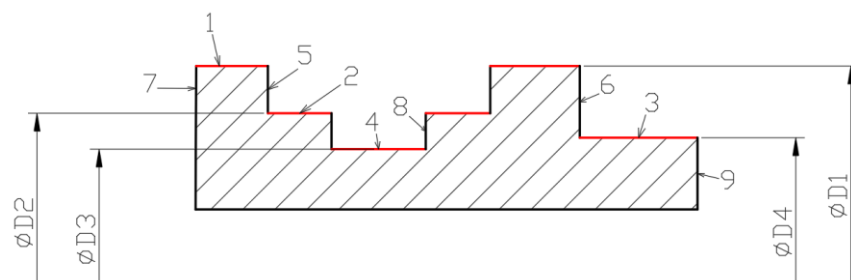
Эскиз детали с изображением измеряемых поверхностей (цифрами обозначены номера поверхностей)
